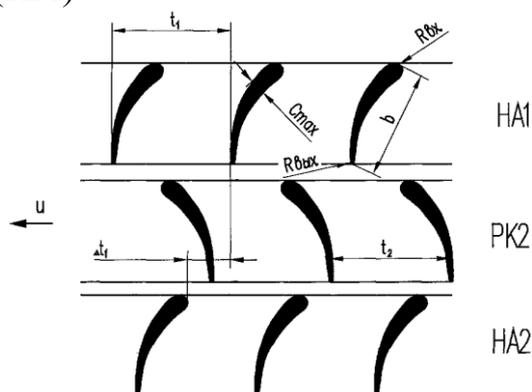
Профиль решёток ступени осевого компрессора:
